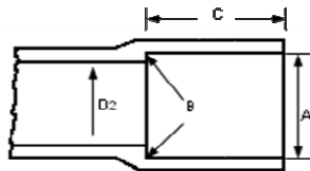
Dimensiones del casquillo formado de tubo de PVC-C
